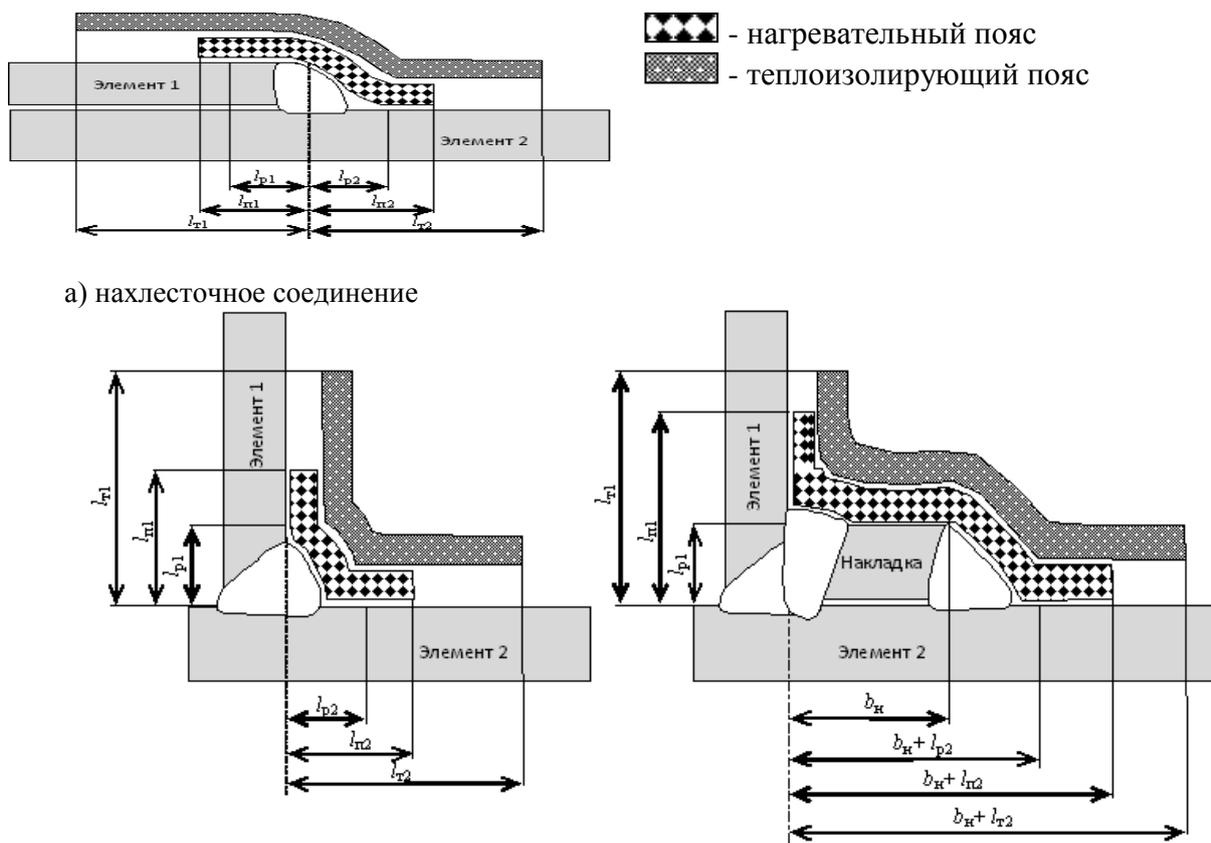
Зоны нагрева при термической обработке нахлесточных и угловых сварных соединений
